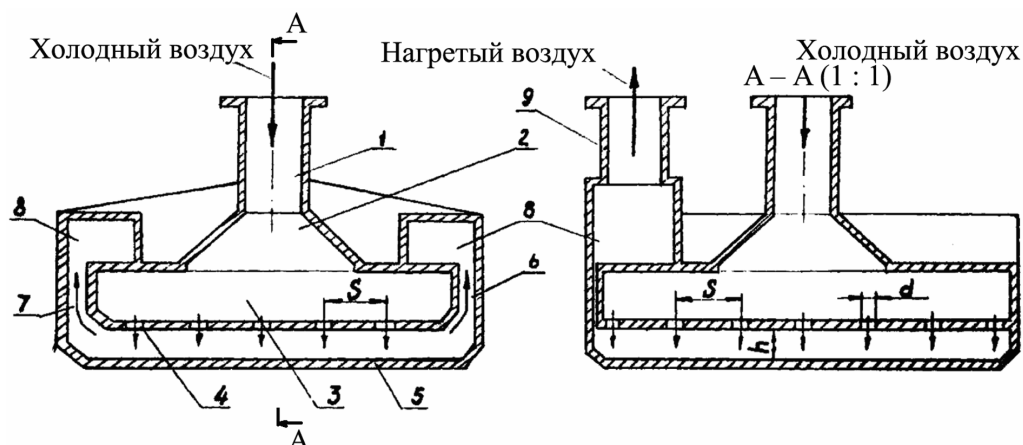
Схема модуля струйного рекуператора конструкции [19] : 1 — подводящий патрубок; 2 — диффузор; 3 — успокоительная камера; 4 — сопла; 5 — поверхность теплообмена; 6, 7 — щели для отвода воздуха; 8 — П-образный воздухоотборник; 9 — отводящий патрубок.
